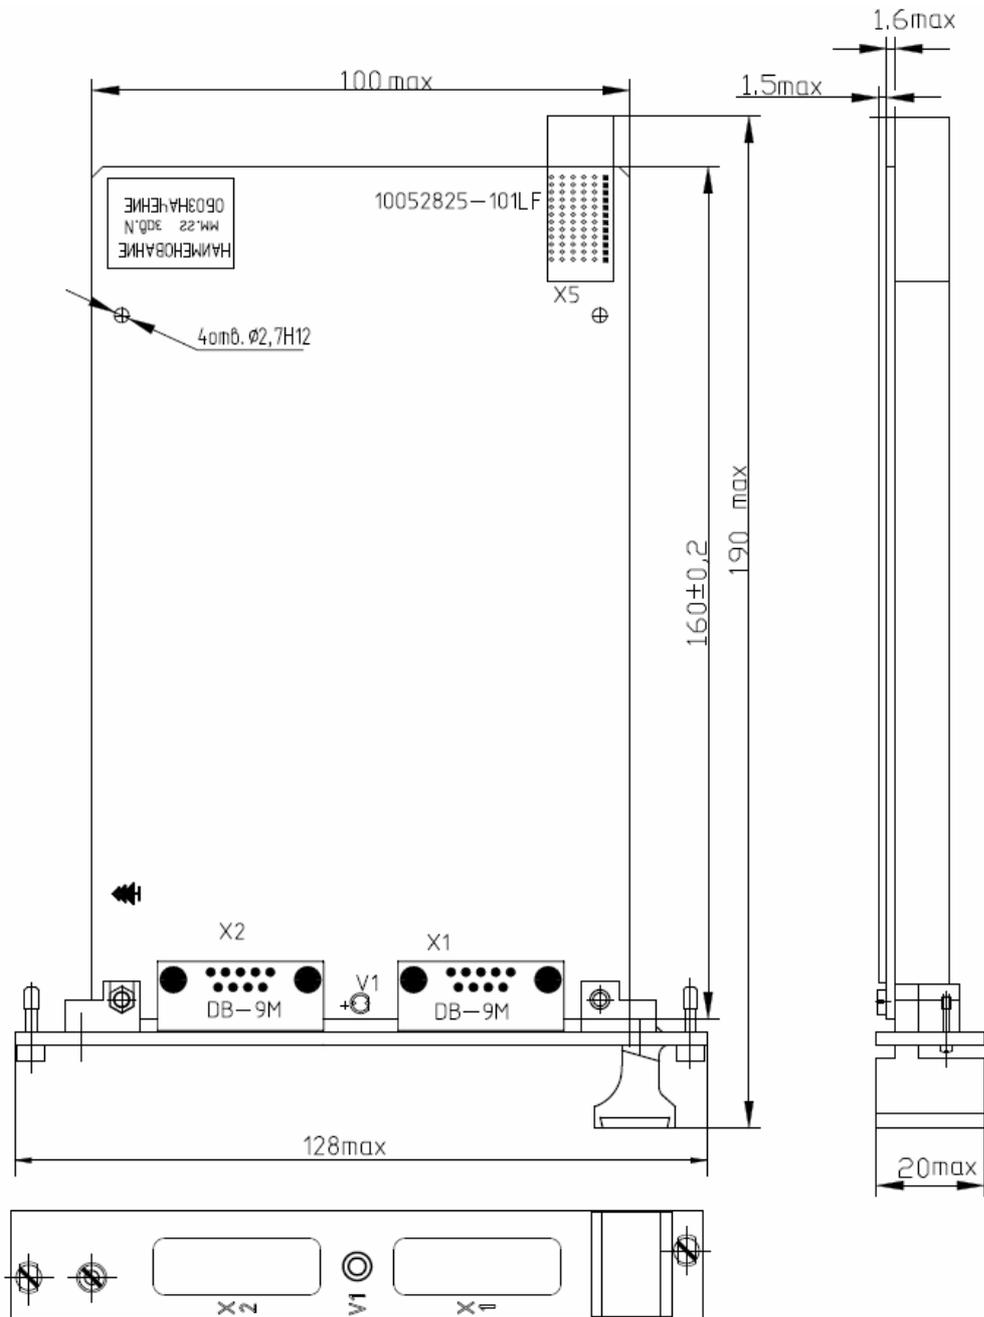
Габаритный чертеж изделия ТА1-3U-CPCIS ГФКП.468351.057-04(-05, -06)
